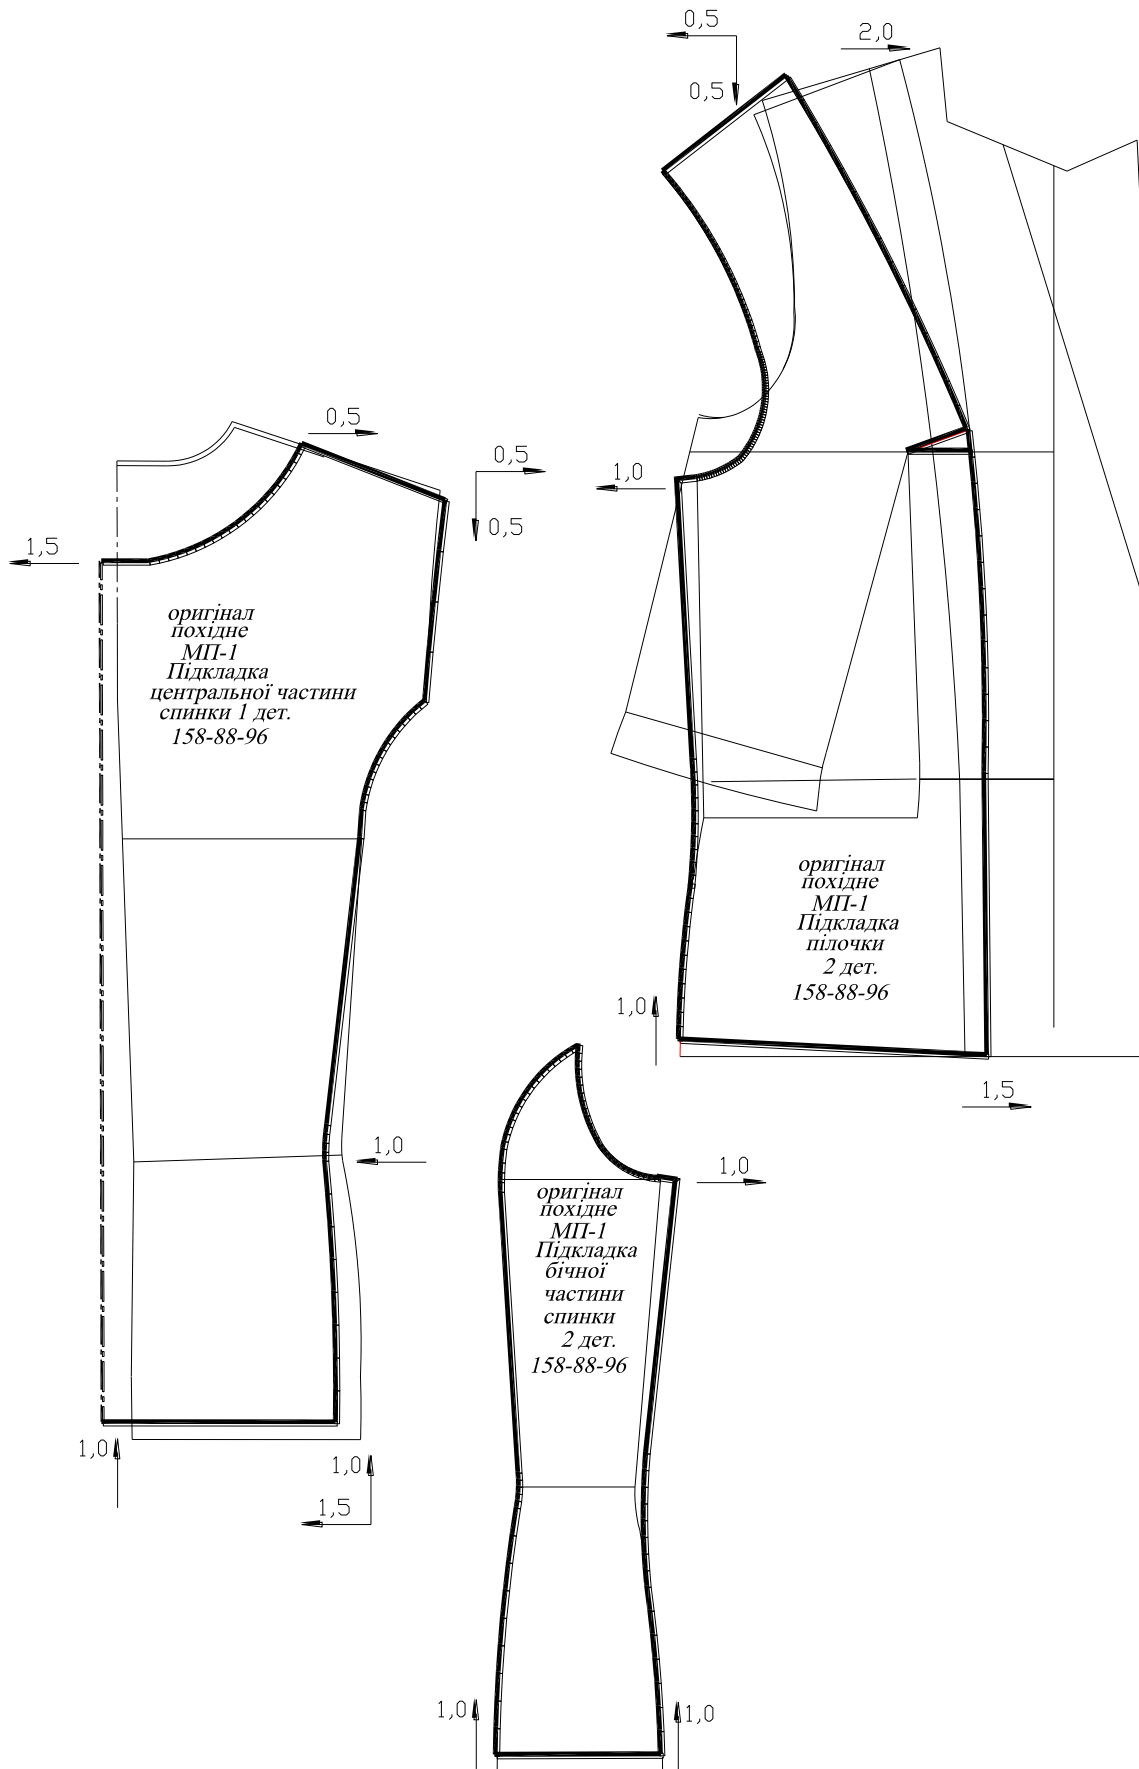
Схеми побудови креслеників похідних лекал підкладки жакета
